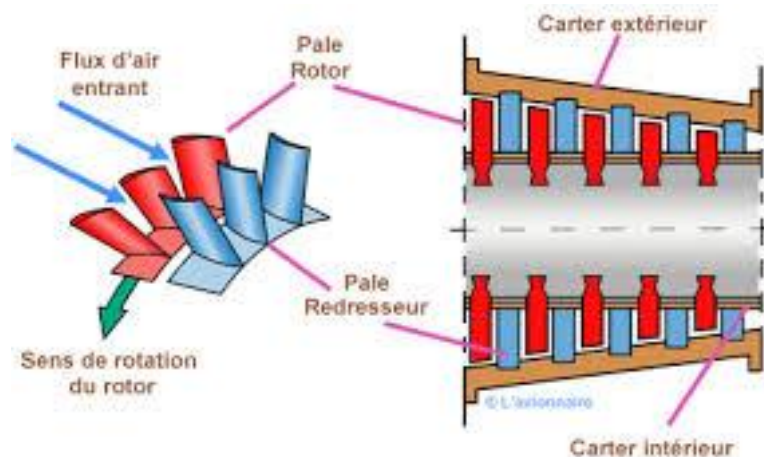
Ensemble du rotor de la turbine vue en coupe
